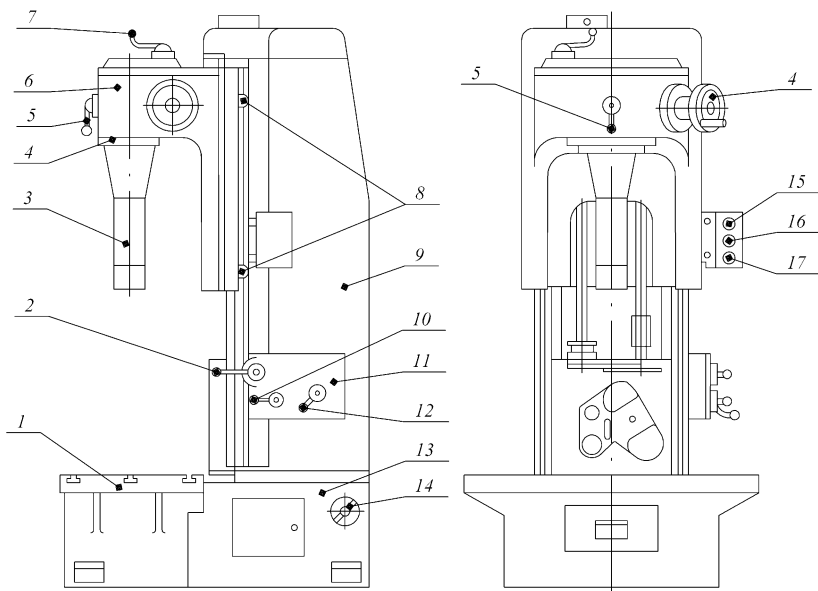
Общий вид вертикально-расточного станка 278Н: 1 – стол; 2 – рукоятка включения рабочего и ускоренного перемещения шпиндельной бабки; 3 – шпиндель; 4 – маховичок ручного перемещения шпиндельной бабки; 5 – рукоятка для отключения шпинделя от кинематической цепи его привода; 6 – шпиндельная бабка; 7 – рукоятка лубрикатора для смазки; 8 – кулачки автоматического выключения перемещения шпиндельной бабки; 9 – колонна; 10 – рукоятка переключения подач шпиндельной бабки; 11 – коробка переключения скоростей и передач; 12 – рукоятка переключения скоростей вращения шпинделя; 13 – основание; 14 – вводный выключатель; 15 – кнопка «Стоп», остановка станка; 16 – кнопка ускоренного перемещения шпиндельной бабки вверх; 17 – кнопка включения вращения шпинделя и рабочей подачи ускоренного перемещения шпиндельной бабки вниз
